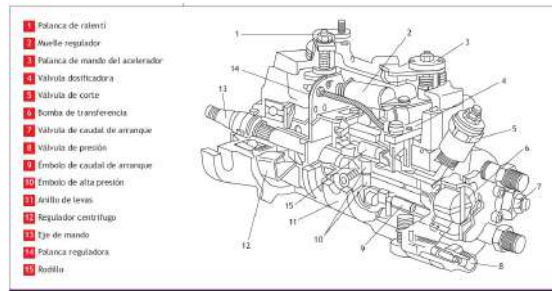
Componentes bomba de inyección de émbolos radiales. (Sanchez, 2009)
